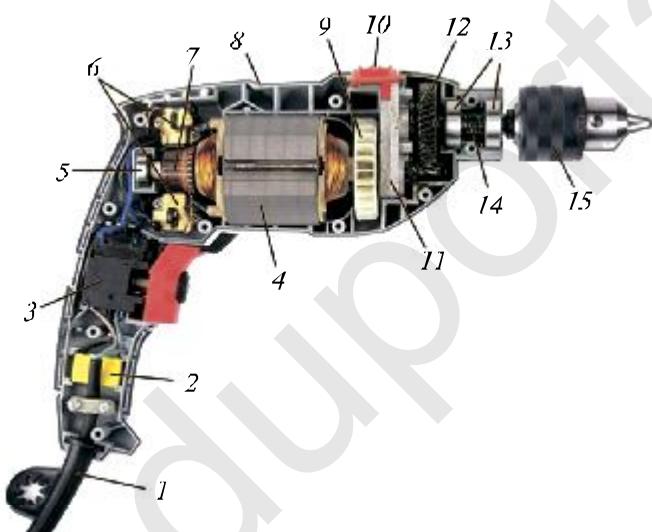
Устройство электродрели: 1 – электрический кабель; 2 – конденсатор; 3 – кнопка регулировки скорости; 4 – электродвигатель; 5 – коллектор; 6 – щетки электродвигателя; 7 – коллектор; 8 – корпус механизма; 9 – вентилятор; 10 – кнопка изменения режимов работы; 11 – редуктор; 12 – крупнозубчатое колесо; 13 – двухзубчатое подающее колесо патрона; 14 – место крепления сверла в патроне; 15 – патрон
